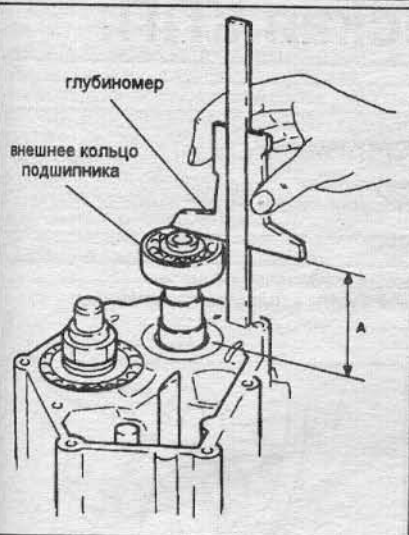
Измерение высоты посадки подшипника вторичного вала (размер А).
